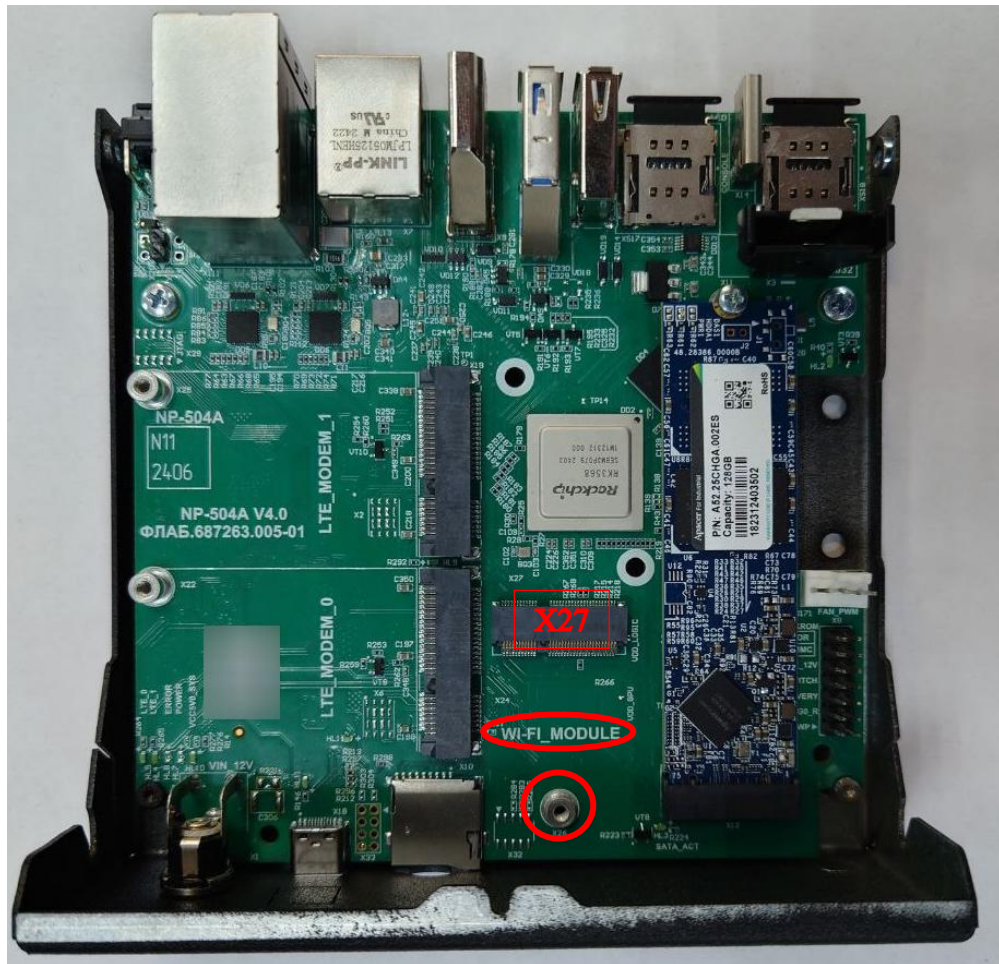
Соединитель X27 для установки Wi-Fi-модема
